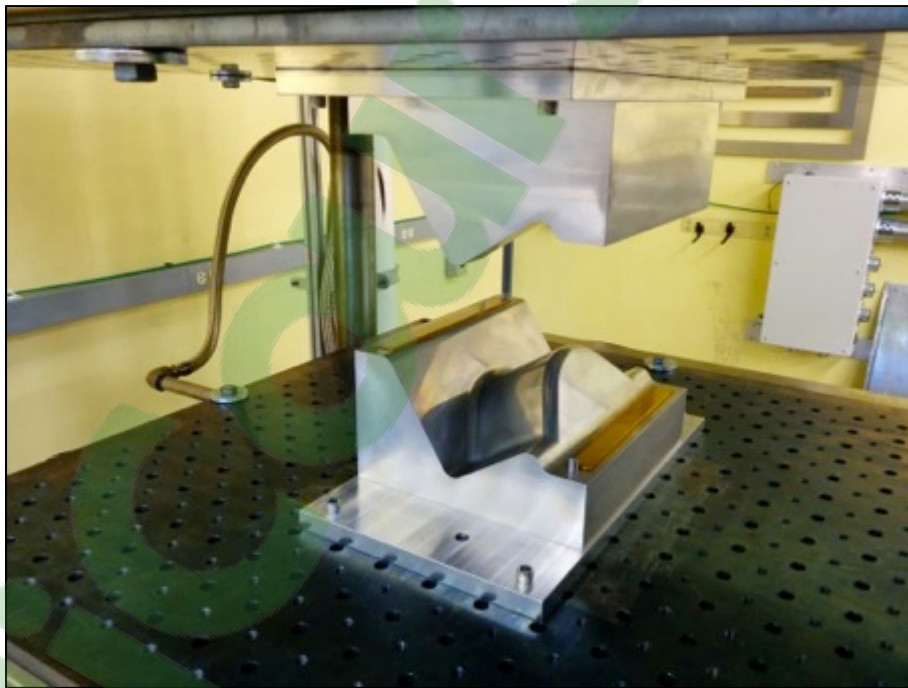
Positionnement du moule T6 dans la presse hydraulique
